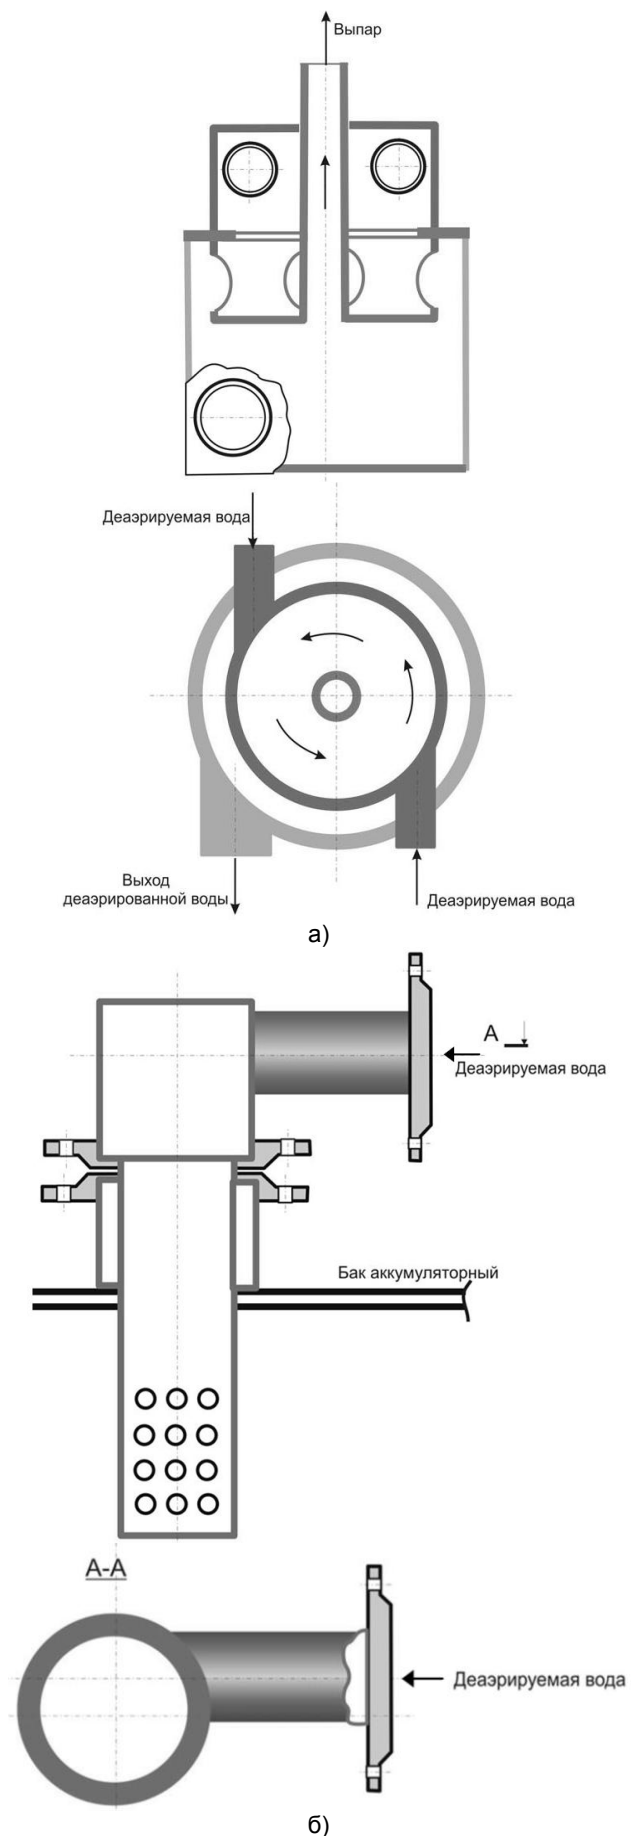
Конструктивные схемы: а – центробежно-вихревого деаэратора; б – капельного
